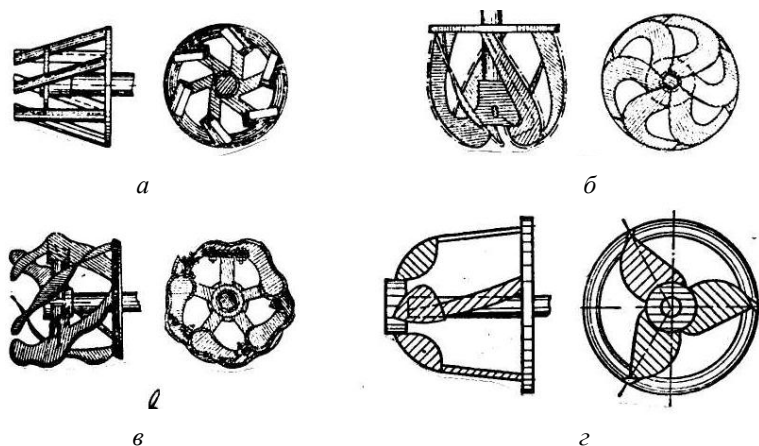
Фрезы наиболее типичных конструкций: *a* – открытая с плоскими ножами; *б* – закрытая (митрообразная) с ножами двойной кривизны; *в* – полуоткрытая с ножами волнообразной формы; *г* – отвально-режущими лопастями
